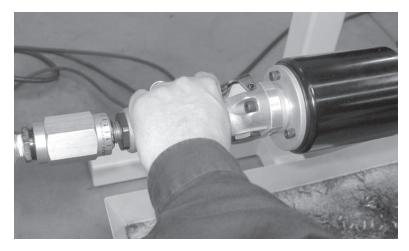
Нажмите пускатель пневматического двигателя для включения станка.
